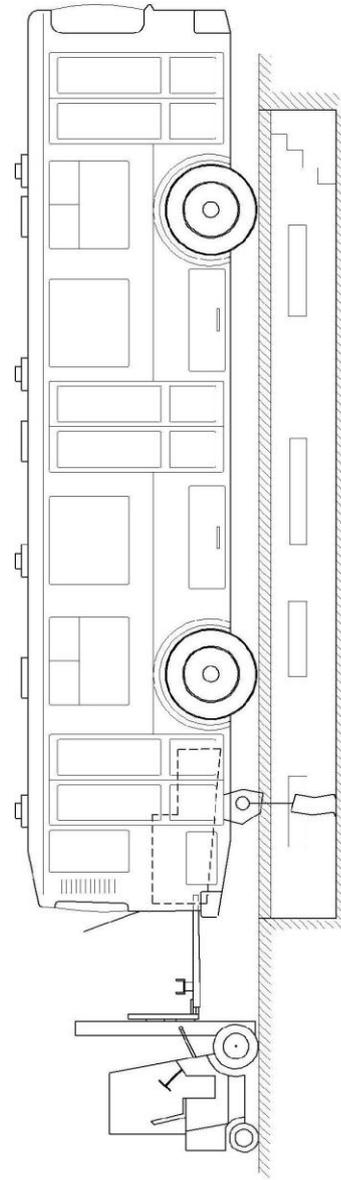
Демонтаж двигателя автобуса НеФАЗ с помощью автоподъемника
